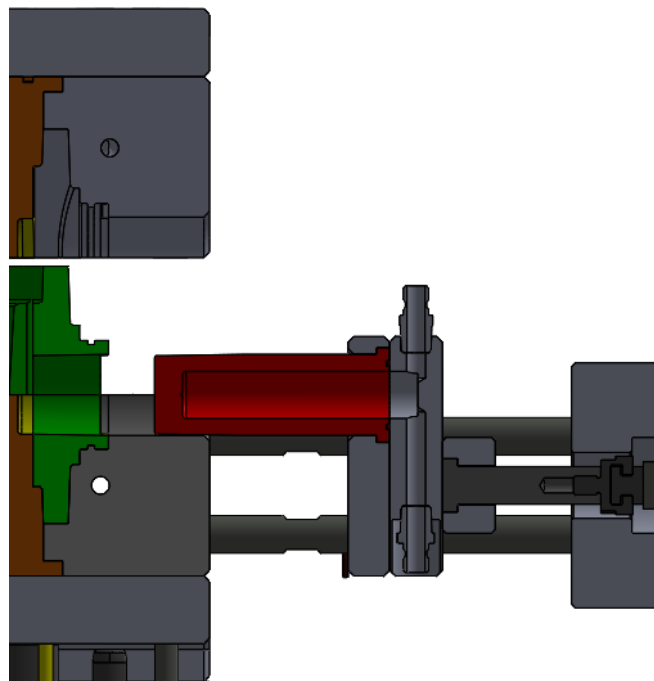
Sistema de Moldeo con Actuador, Molde Abierto
